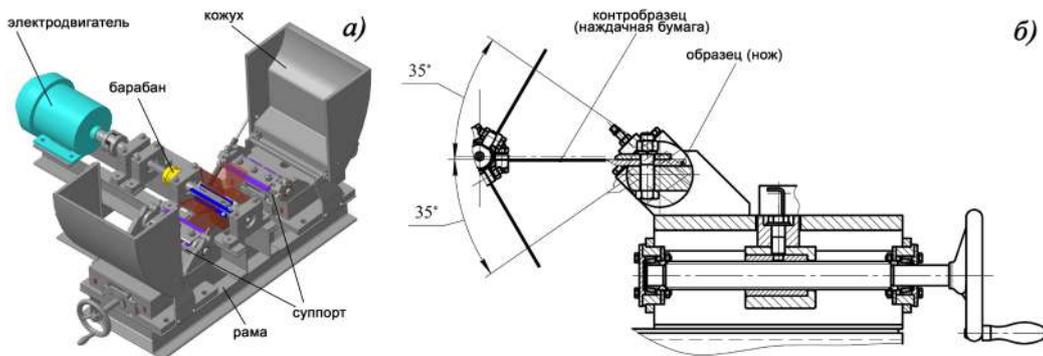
Схема расположения основных узлов стенда УИН (*а*) и схема установки образцов и контрольных образцов (*б*)
